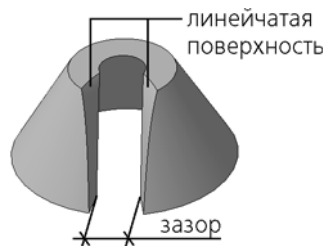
Кромки стыка при размещении зазора на конической обечайке способом перпендикулярно поверхности листа
